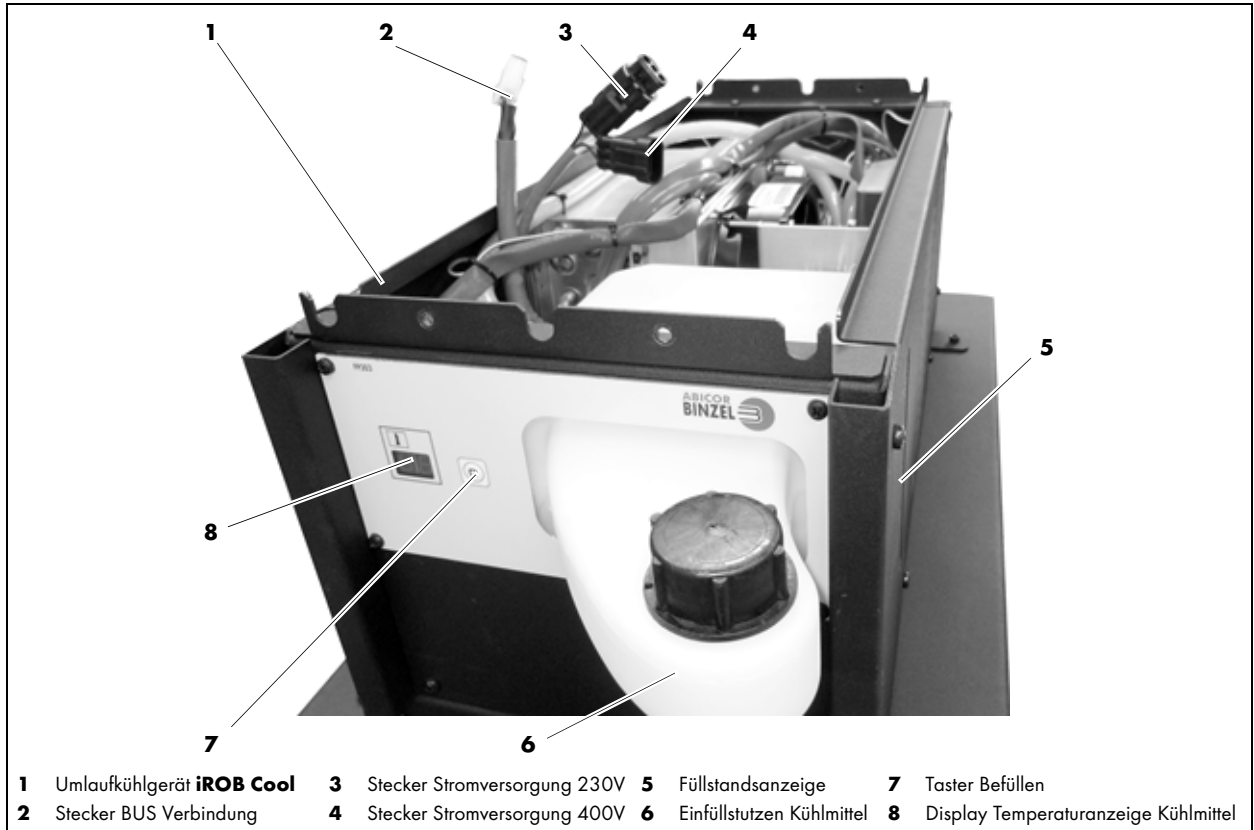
Komponenten Umlaufkühlgerät iROB Cool
